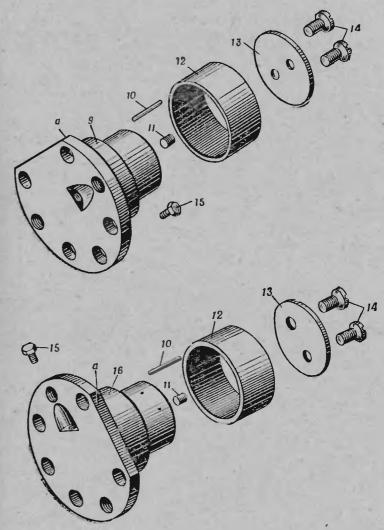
Цапфы; 9 — левая цапфа; 10 — игла; 11 — виит; 12 — втулка; 13 — шайба; 14 — винты; 15 — пробка; 16 — правая цапфа; а — скос
